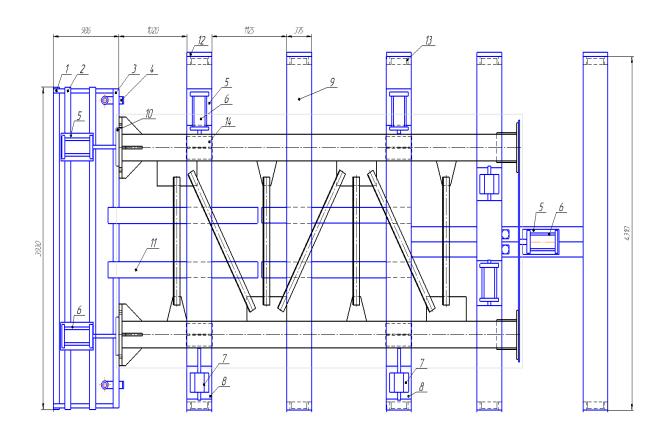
Сборочно-сварочный кондуктор
